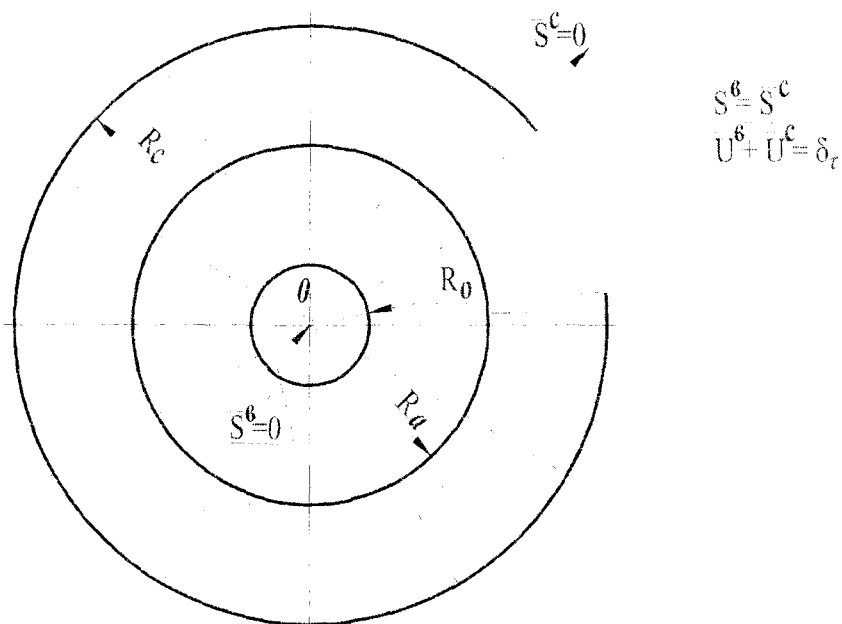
К решению задачи Ляме о соединении цилиндрического вала со ступицей
